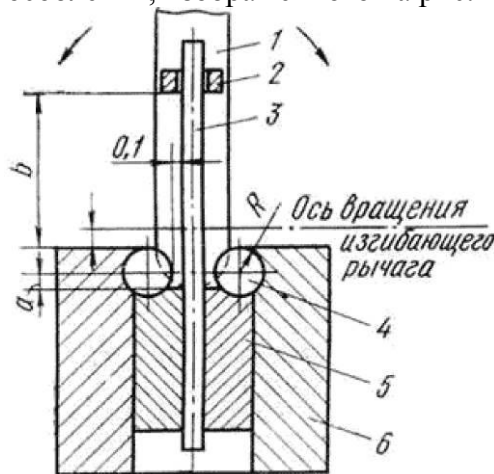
Схема испытания на перегиб 1 – рычаг; 2 – сменный поводок; 3 – образец; 4 – валики; 5 – губки; 6 – тиски
